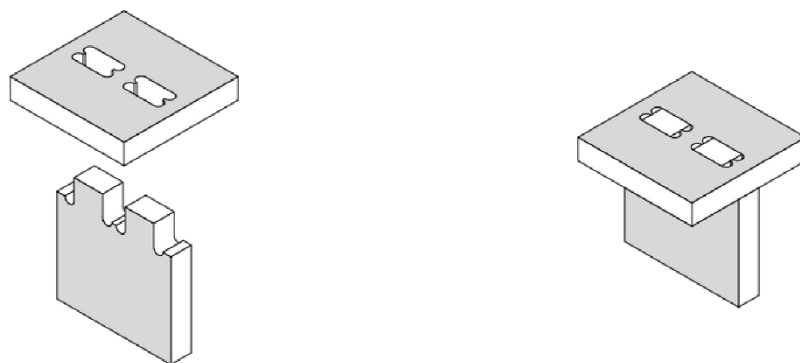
Fuente Opendesk - Digital woodworking- remastering traditional joints
